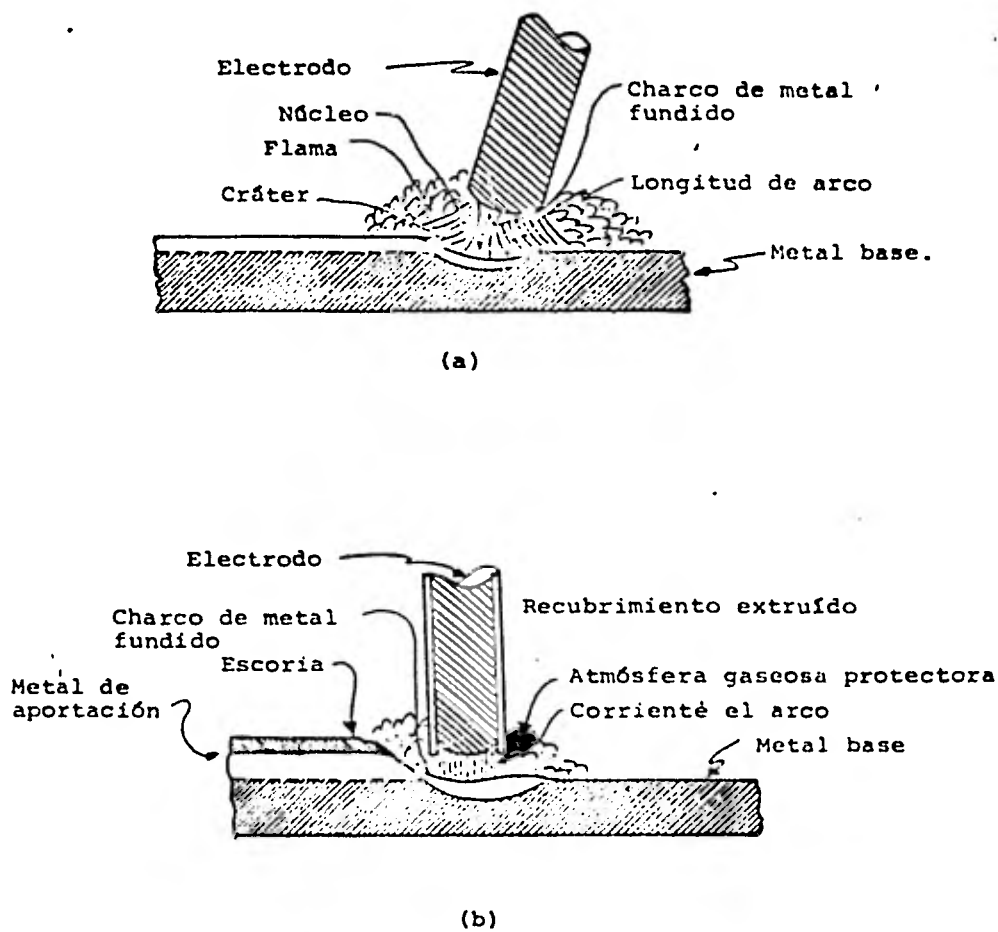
Soldadura de arco. (a) sin protección
